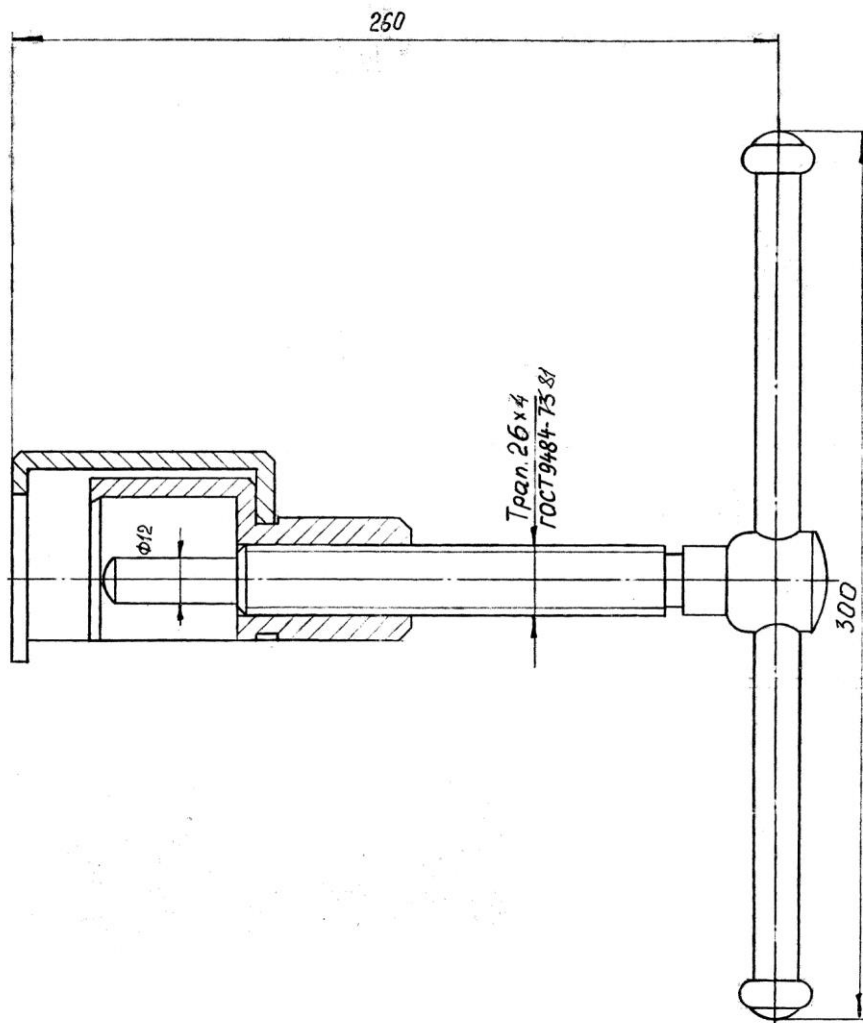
ЗМ 7814-5118, Съемник звездочки и втулки коленчатого вала
